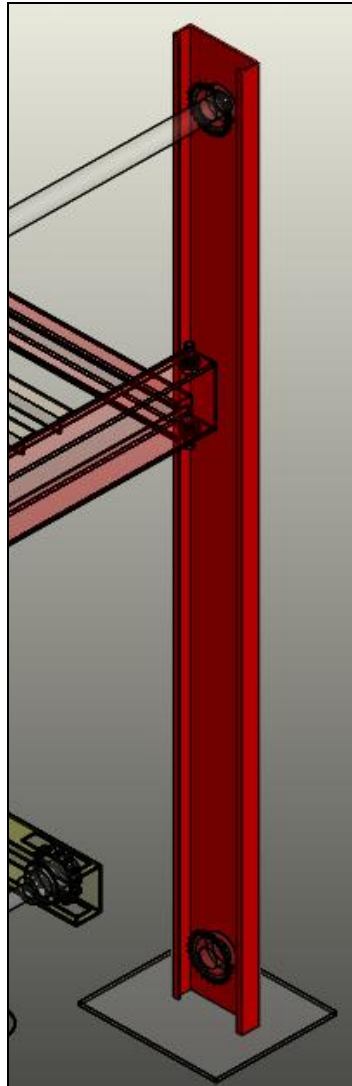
COLUMNA DEL SISTEMA
